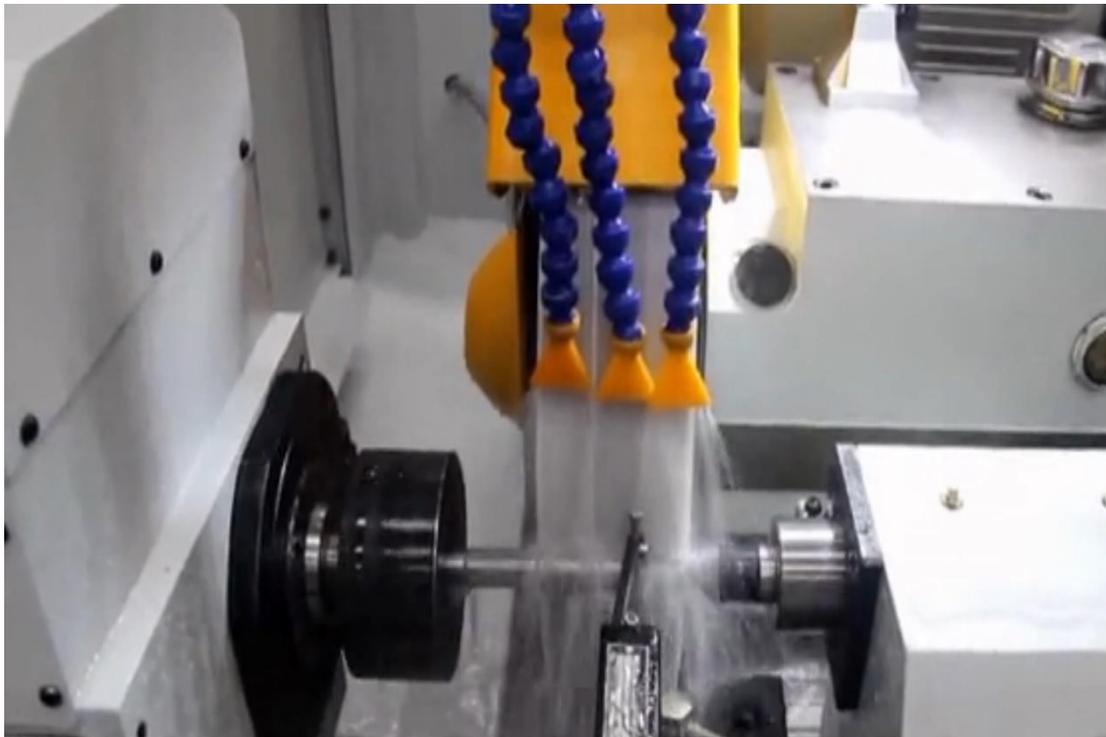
Bearbeitung mit CNC-Rundschleifmaschine^[13]
